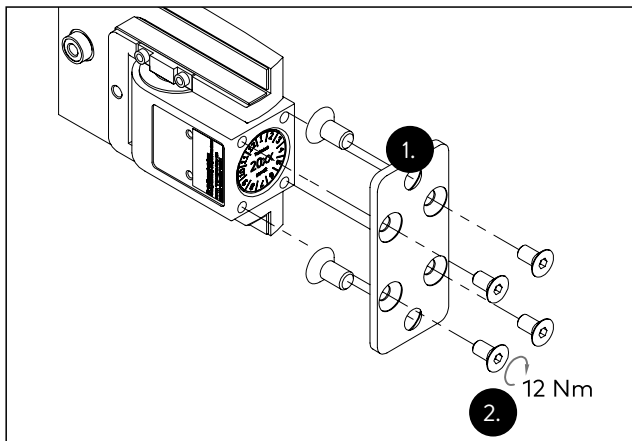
Fissaggio dei pannelli di montaggio sulla cerniera per porta a vento
